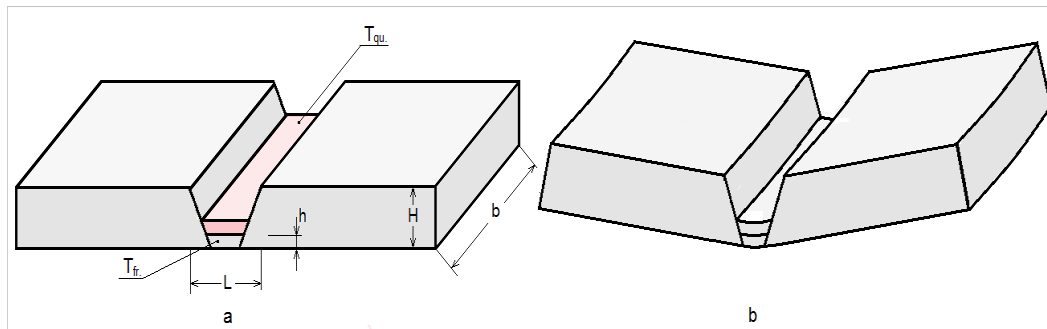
Deformações das chapas soldadas causadas pela contração do metal do cordão do solda: a – estado hipotético; b – estado real deformado; Tfr. – Temperatura do metal frio após primeiro passe de solda; Tqu. – Temperatura do metal quente no momento do segundo [47].
